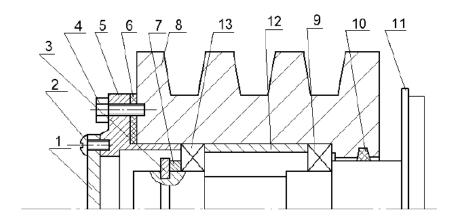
Эскиз сборочной единицы: 1 — крышка; 2 — винт(2 шт.); 3 — кольцо стопорное; 4 — болт(4 шт.); 5 — фланец;
